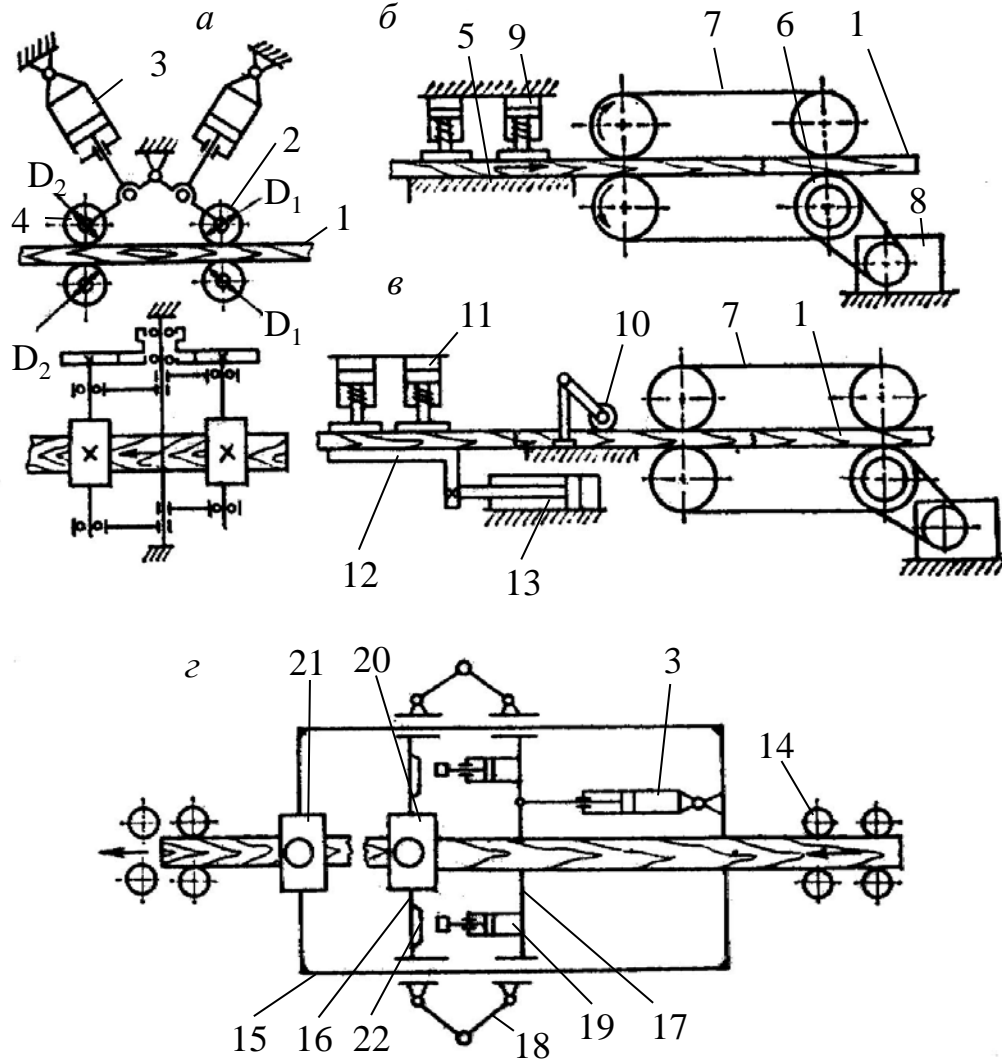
Схемы прессов для продольного сжатия заготовок:
